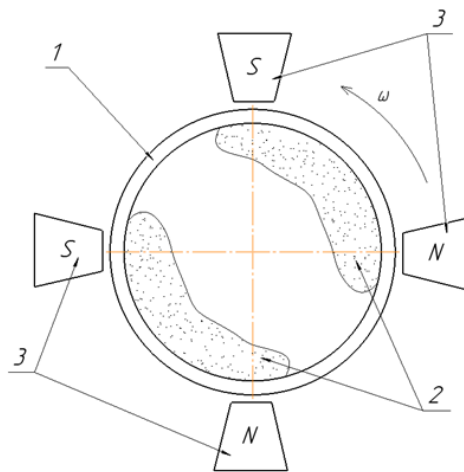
Схема МАО внутрішніх поверхонь обертання
